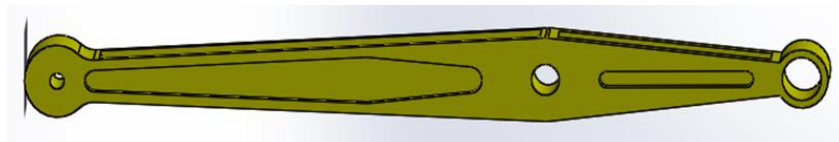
Barra o strut longitudinal, FUENTE: SOLIDWORKS
